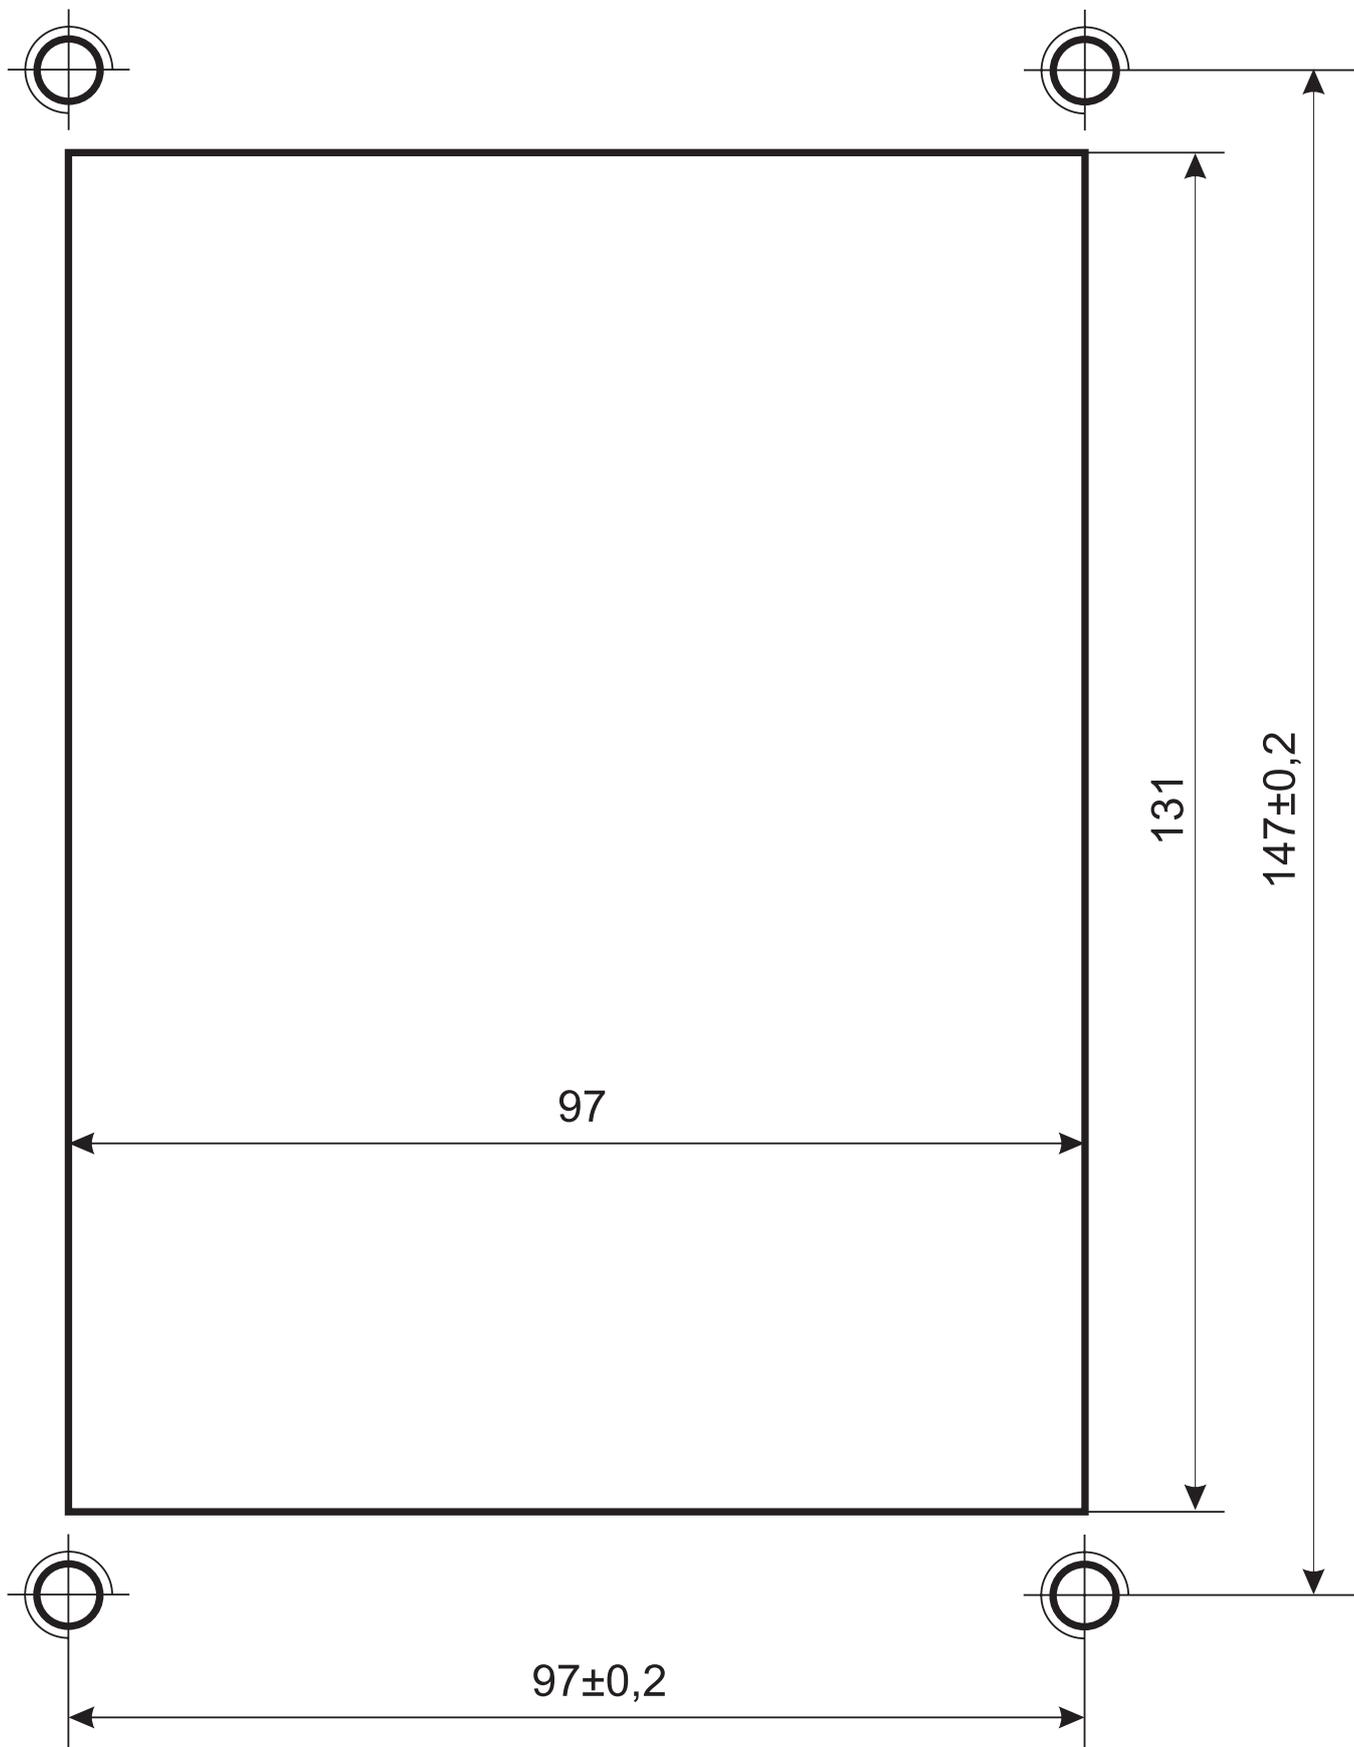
Разметка отверстий для крепления контроллера PERCo-SC-600PDP (PERCo-SC-600PDPV)
